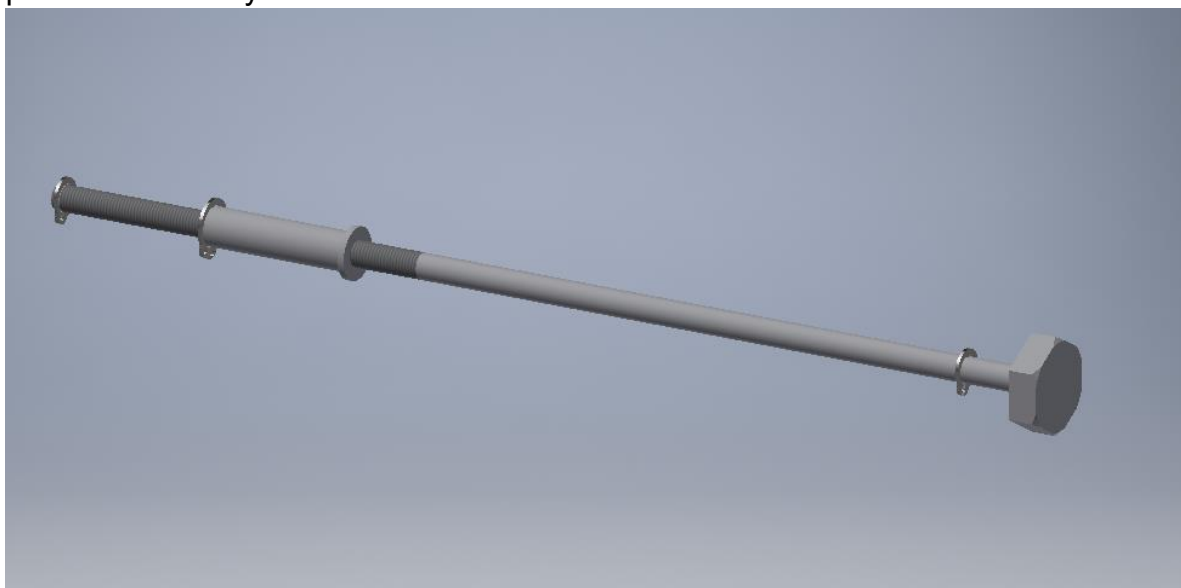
Detail rámu pripojenia ďalšieho boxu
